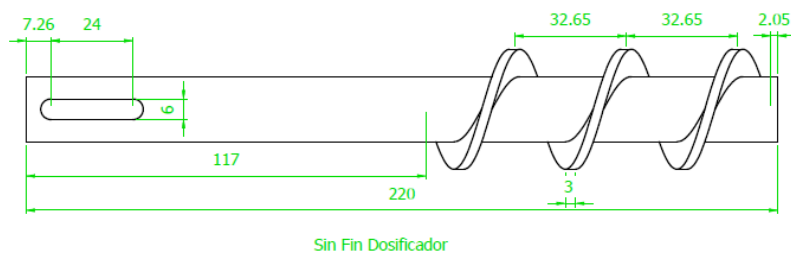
Diseño del tornillo sinfín por parte del fabricante
